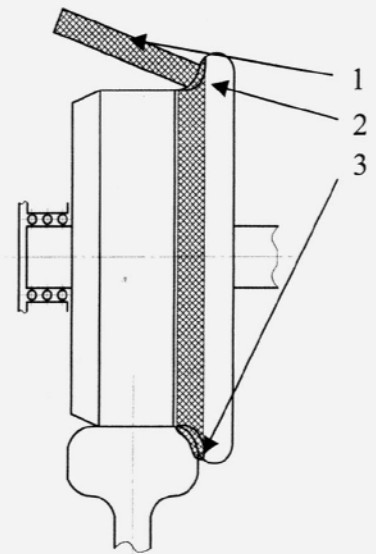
Стержневой гребнерельсо-смазыватель: 1 – смазочный стержень, 2 – гребень колеса, 3 – боковая поверхность головки рельса
